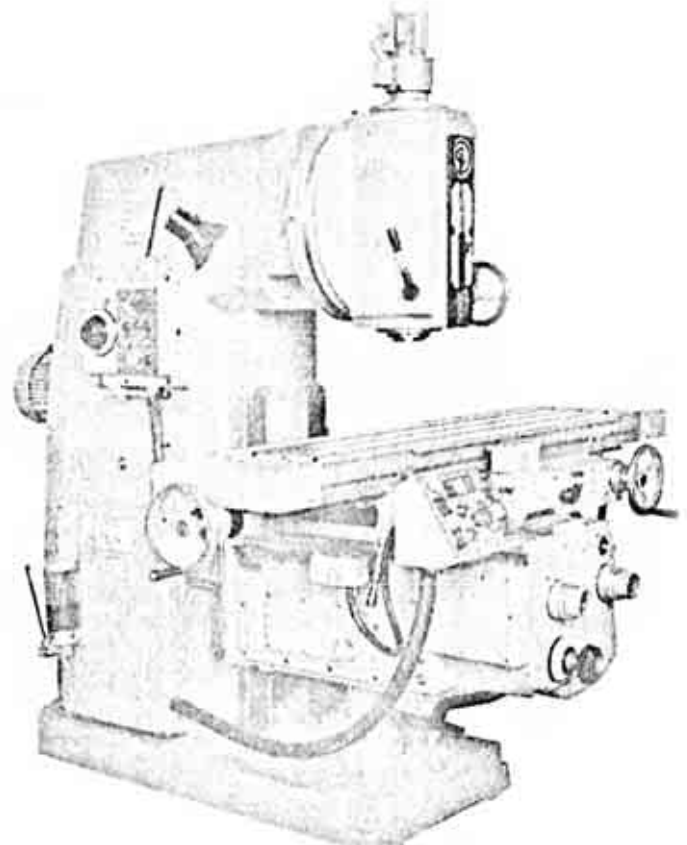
Вертикальный консольно-фрезерный станок 6Т13
